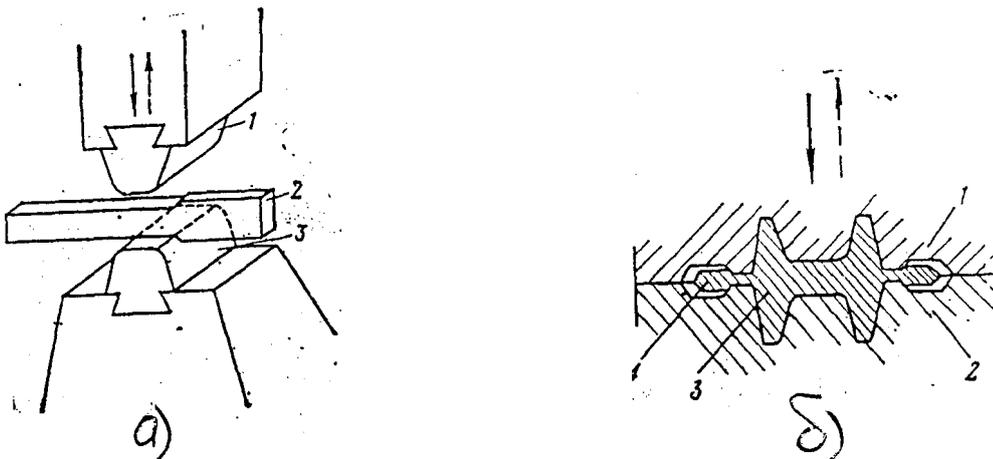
Обработка металлов ковкой и горячей штамповкой:
